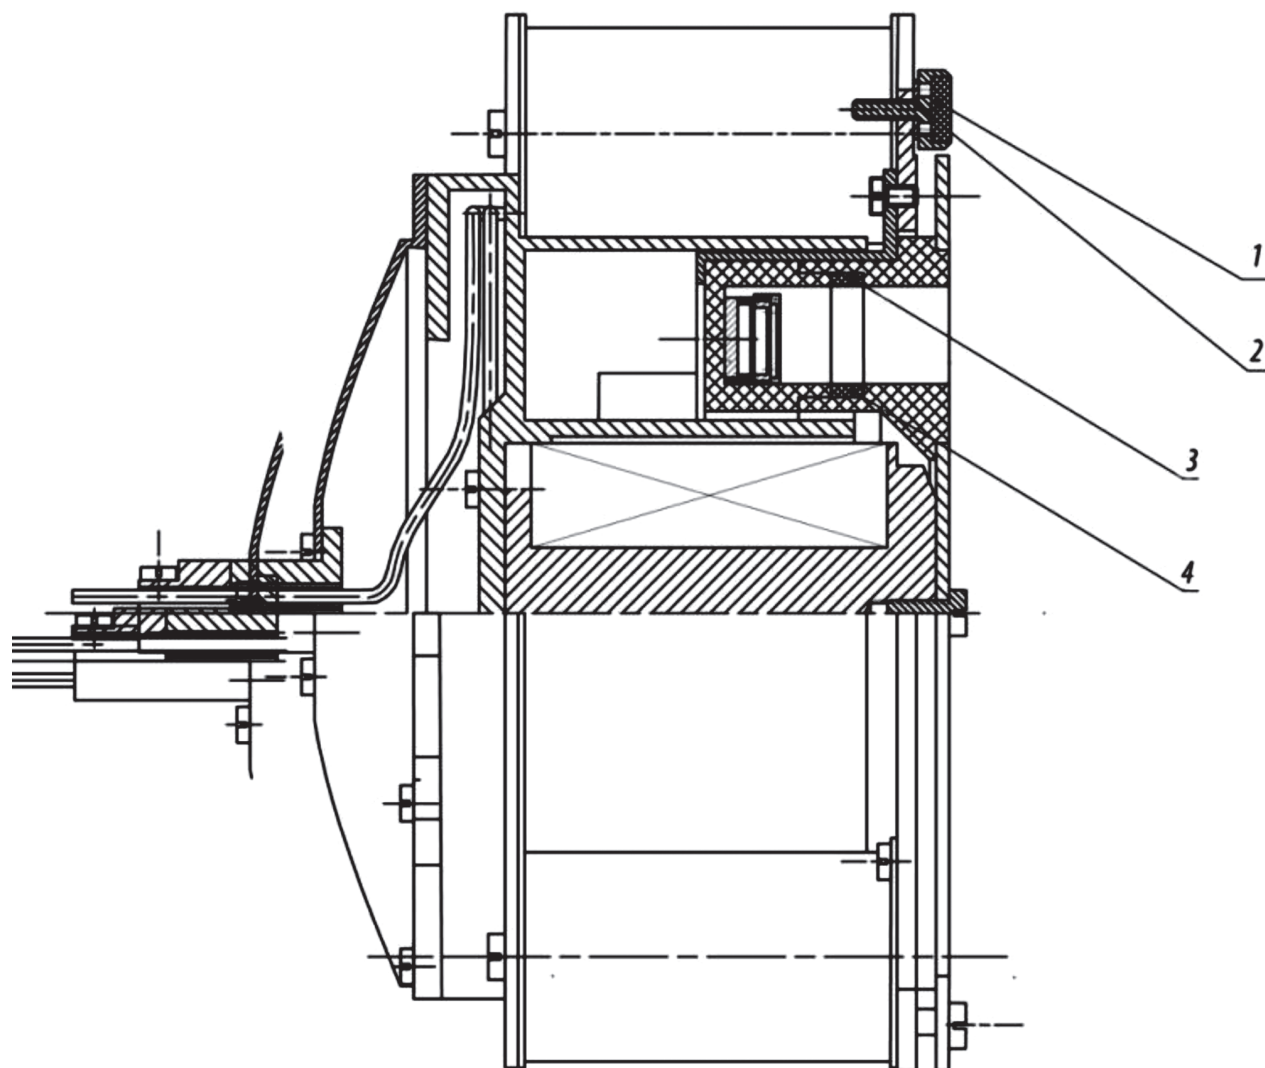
Доработанная модель двигателя СПД-100 и контрольные образцы для измерения скорости напыления: 1 — наружный КО; 2 — держатель образца; 3, 4 — внутренние КО
